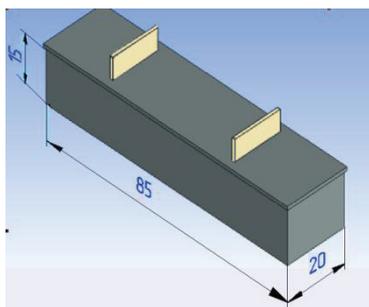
Форма с подготовленными полосками фольги, установленными в рези пластинки
